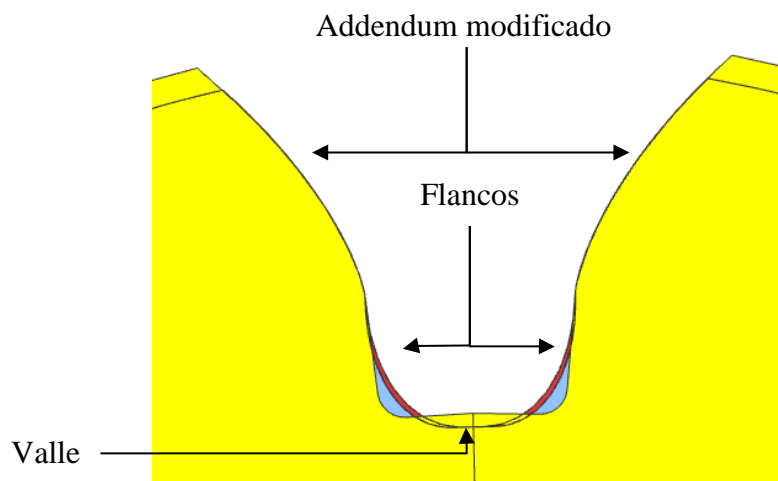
Superposición de los engranajes del acelerador de diseño y el generado desde Excel®
